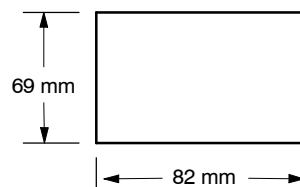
Dimensiones para cortar una abertura en la superficie de montaje del TD 100C
